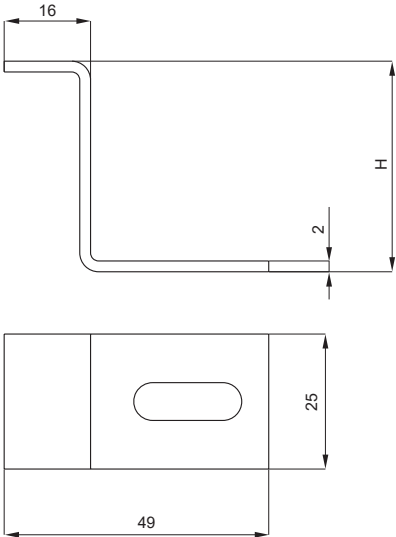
Скоба для крепления лотка с крышкой / Figure B.1 – C-clamp for cable tray with cover
